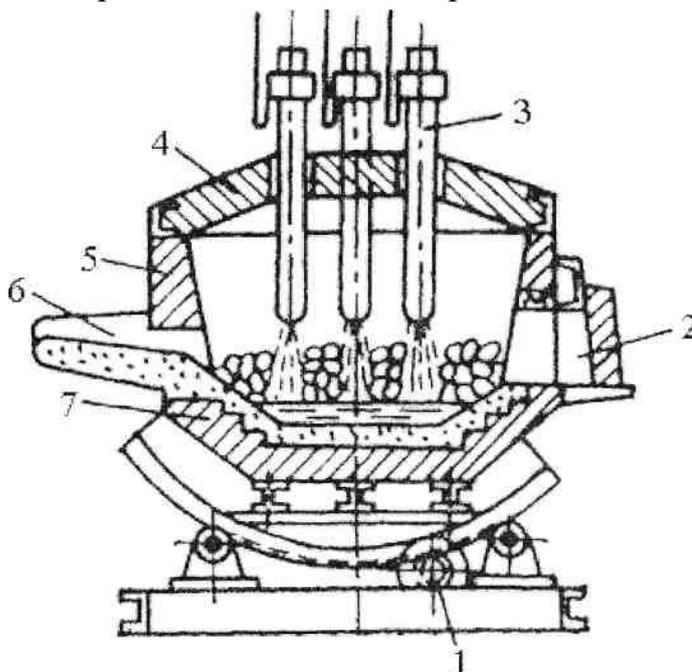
Схема трехфазной дуговой печи: 1 - механизм поворота печи; 2 - загрузочное окно; 3 - электроды; 4 - свод; 5 - корпус; 6 - желоб для выпуска стали; 7 - под печи
